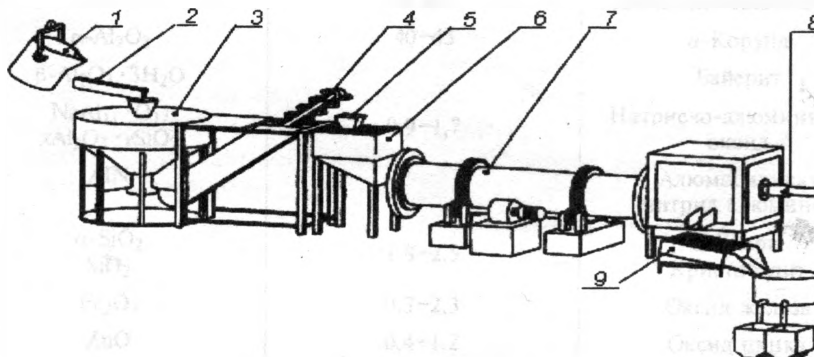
Схема комплекса оборудования для литья дробы мод.46145: 1— ковш; 2— желоб металлоприемника; 3— дробелитейная машина; 4— наклонный элеватор; 5— приемная воронка; 6— бункер печи; 7— барабанная печь; 8— блок горелочной печи; 9— агрегат рассева дробы
